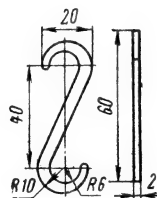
Серьга типа У776 для крепления светильников к закладным коробкам.
